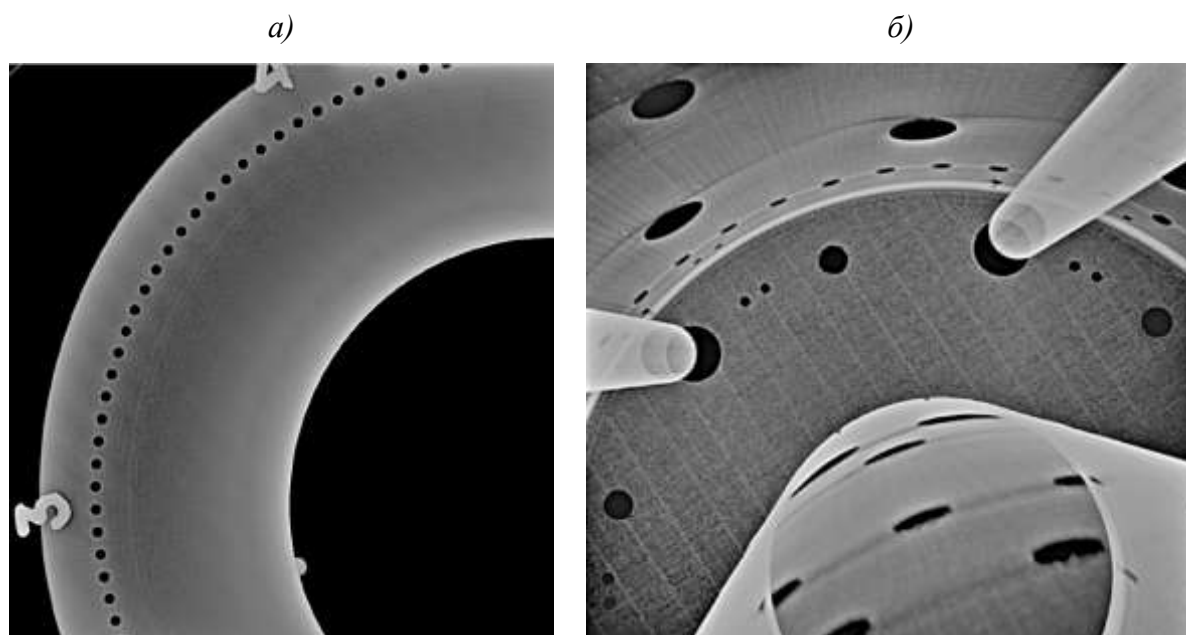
Цифровые рентгенограммы заготовок деталей, полученных методом АТ с высокой шероховатостью поверхности (*а* – заготовка детали фронтное устройство двигателя МГТД-125Э из сплава ВЖ159; *б* – заготовка детали жаровая труба двигателя МГТД-10 из сплава ВЖ159)
